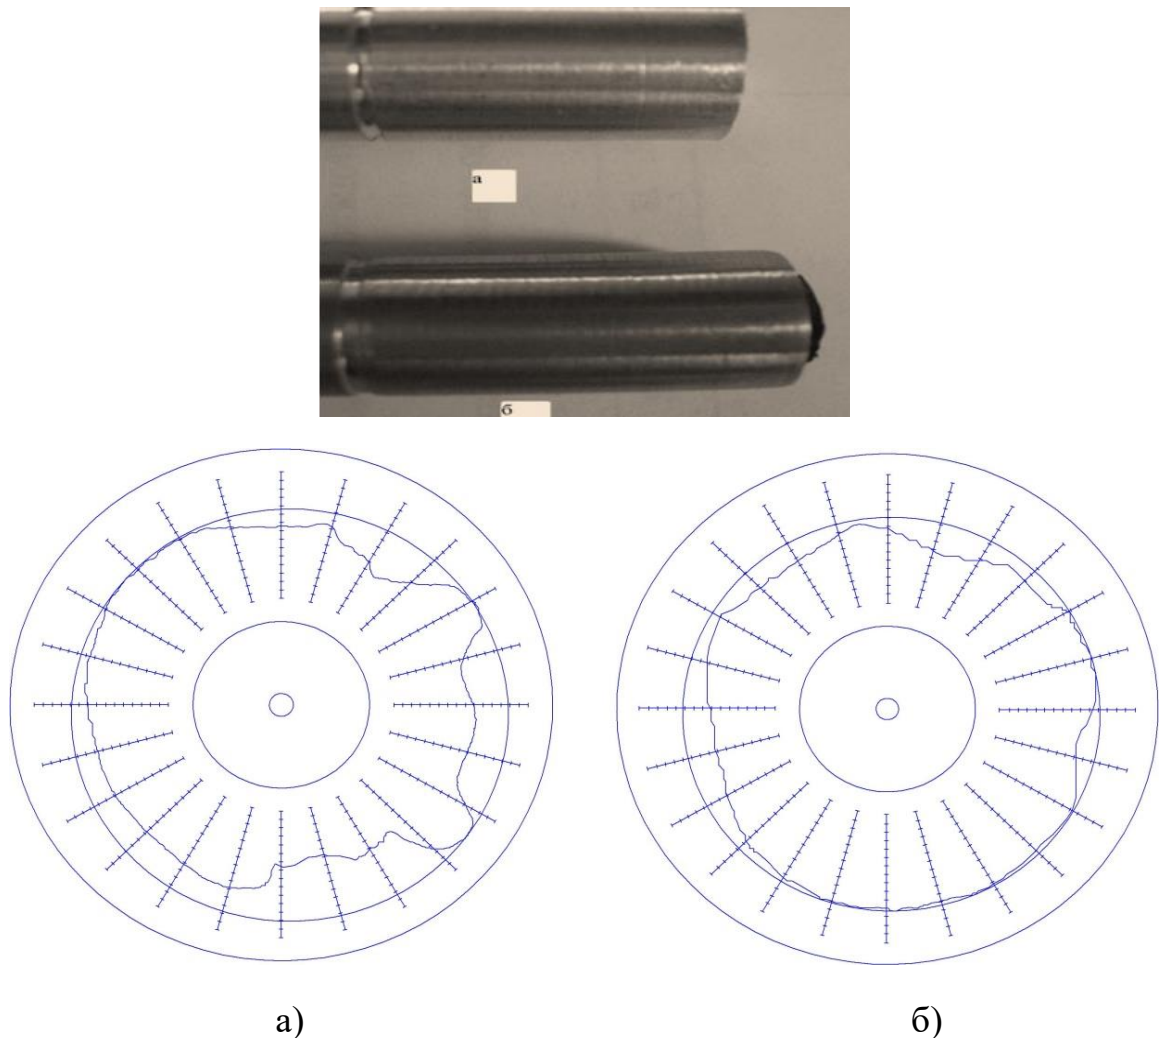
Зразки оброблених деталей і круглограм для порівняння похибок обробки при а) одно різцевому точінні оброблюваної заготовки і б) дворізевої обробці з використанням самоналагодження
